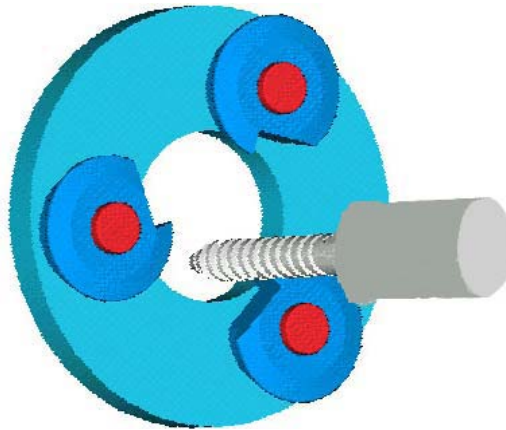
Accesorio con herramientas de forma para roscado por remolino.
